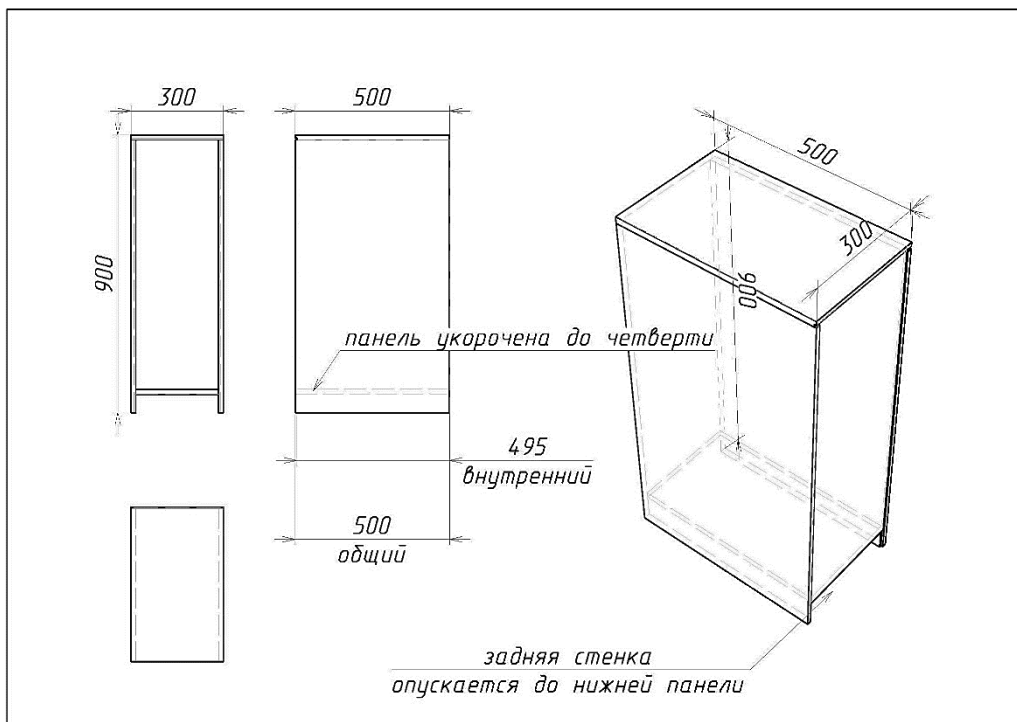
Установка задней стенки в четверть в корпус с накладной крышкой и вкладным дном (БМ)
